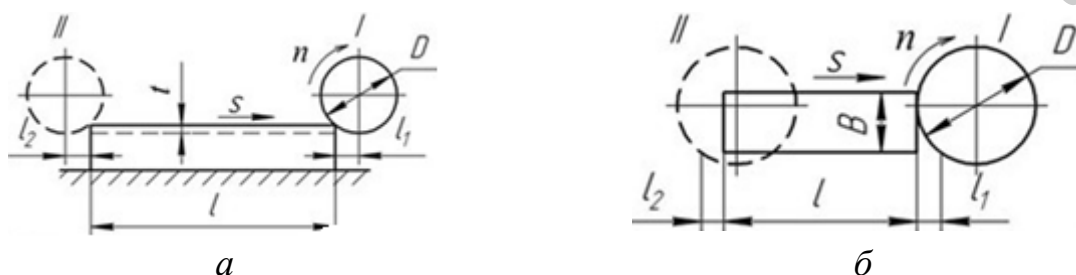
Схемы расчета величины врезания и перебега при фрезеровании: а – концевой фрезой; б – несимметричной торцевой фрезой
